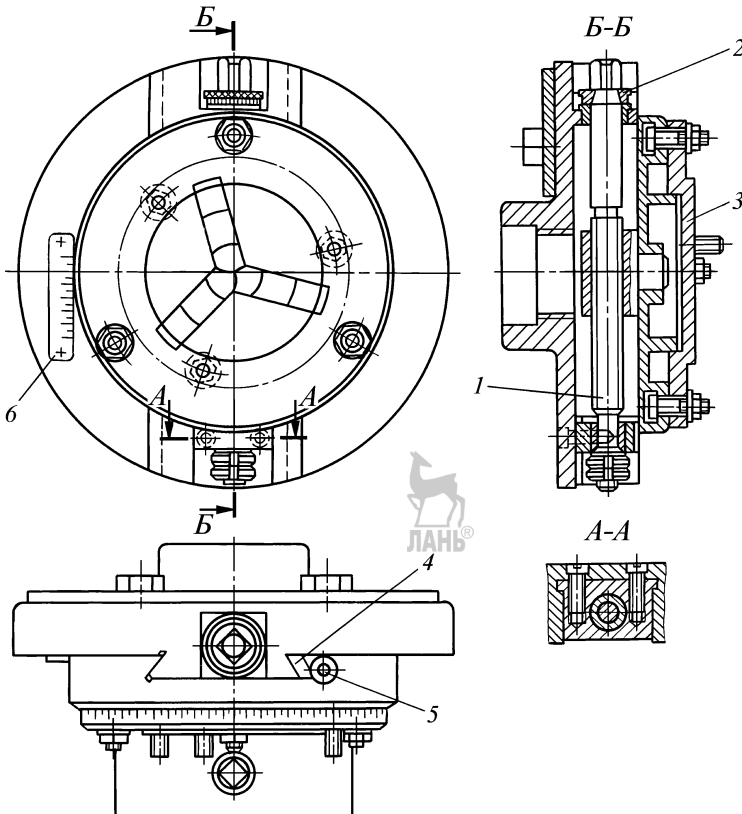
Приспособление для обработки эксцентриковых заготовок
